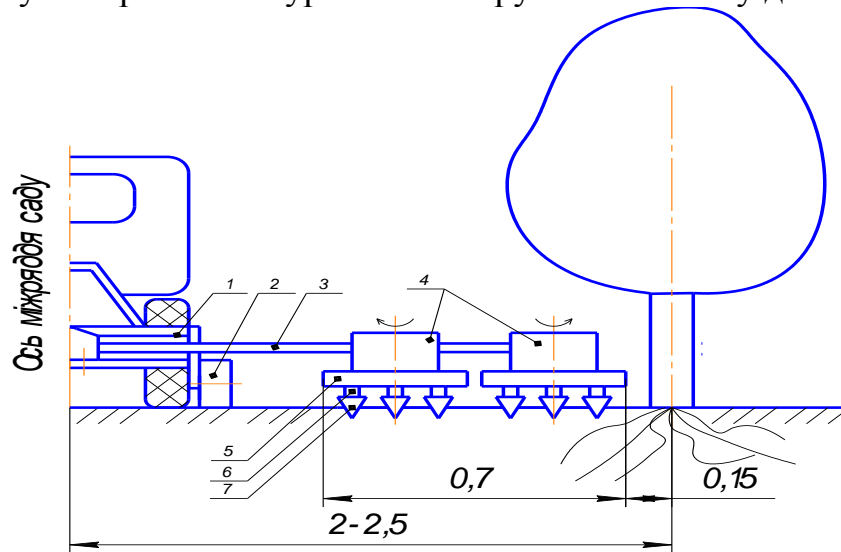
Конструктивно – технологічна схема фрезерної машини:
